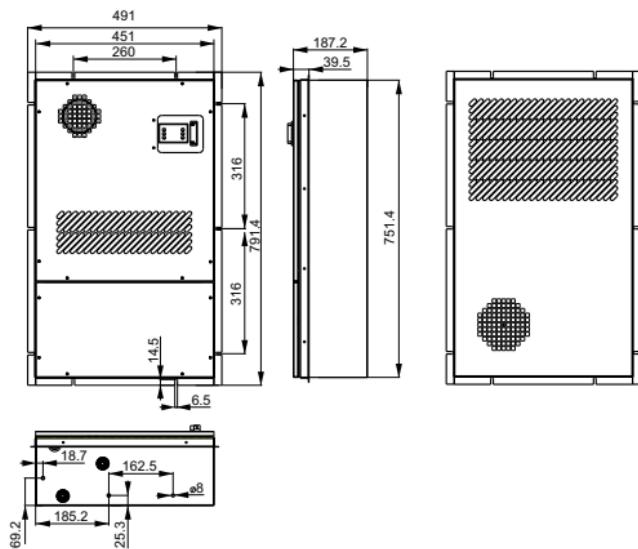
Внешний вид и габаритные размеры моделей СМ-1000-230 и СМ-1500-230 /
